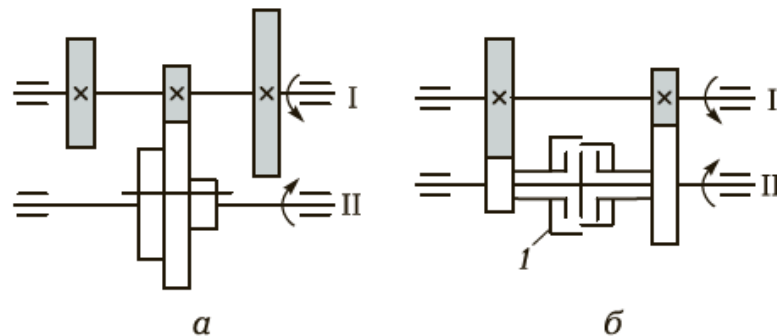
Схемы двухваловых передач коробок скоростей с подвижным блоком зубчатых колес (а) и с муфтой (б):
